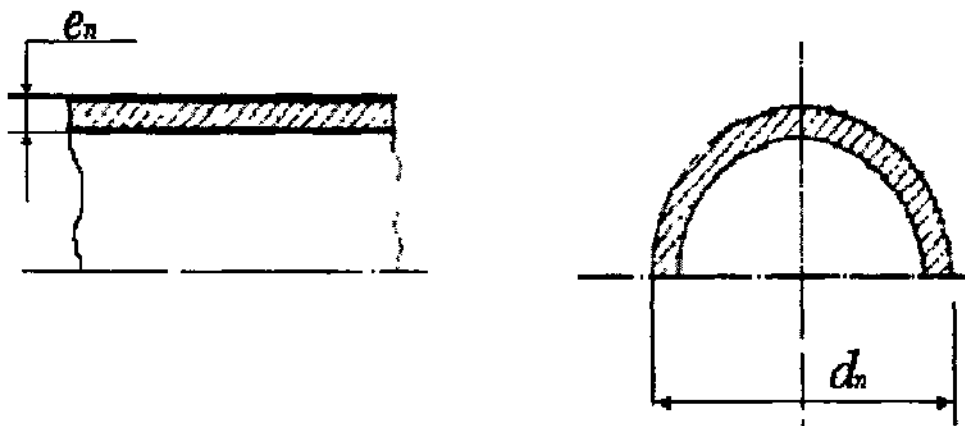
Повздовжній і поперечний перерізи труб (без розтруба) та гладкої частини труб розтрубних
